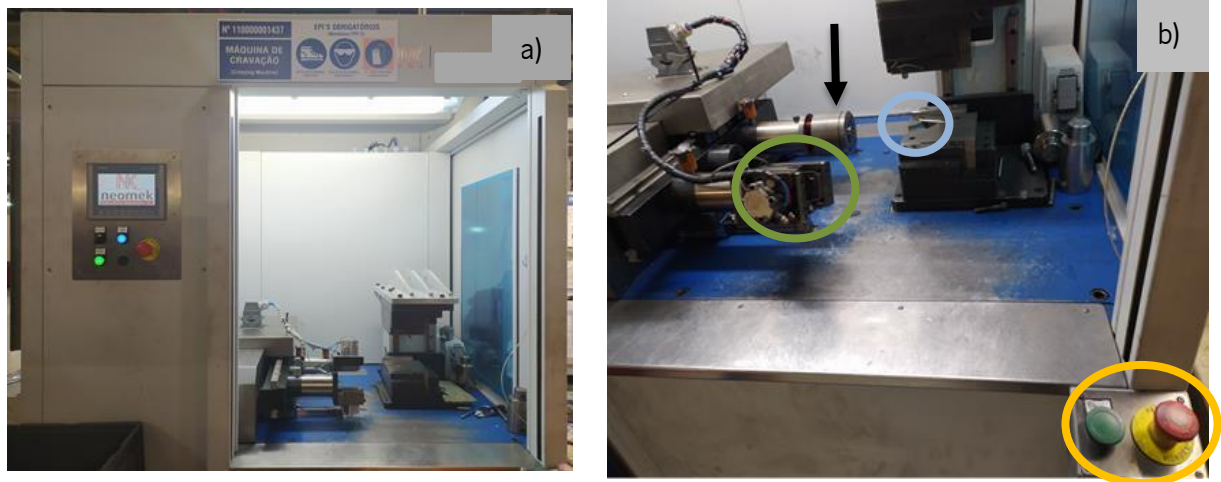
a) Máquina Neo b) Máquina com os locais de inserção de material salientados
